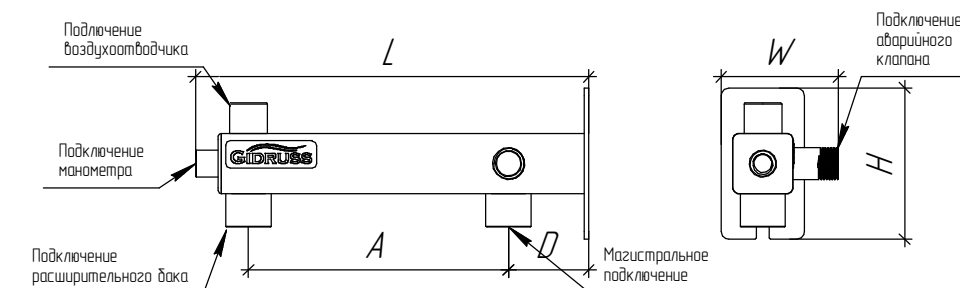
Габаритно-присоединительные размеры основания консоли для расширительного бака BKSS-24D.BASIS
